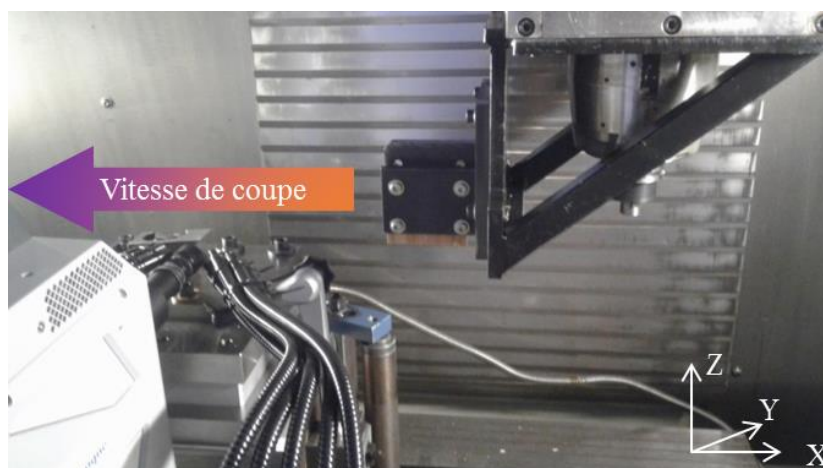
Vue d'ensemble du montage et du mouvement de l'échantillon.
